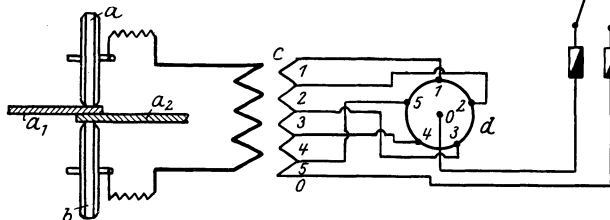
Schaltung und Stromzuführung bei Nahtschweißmaschinen.
